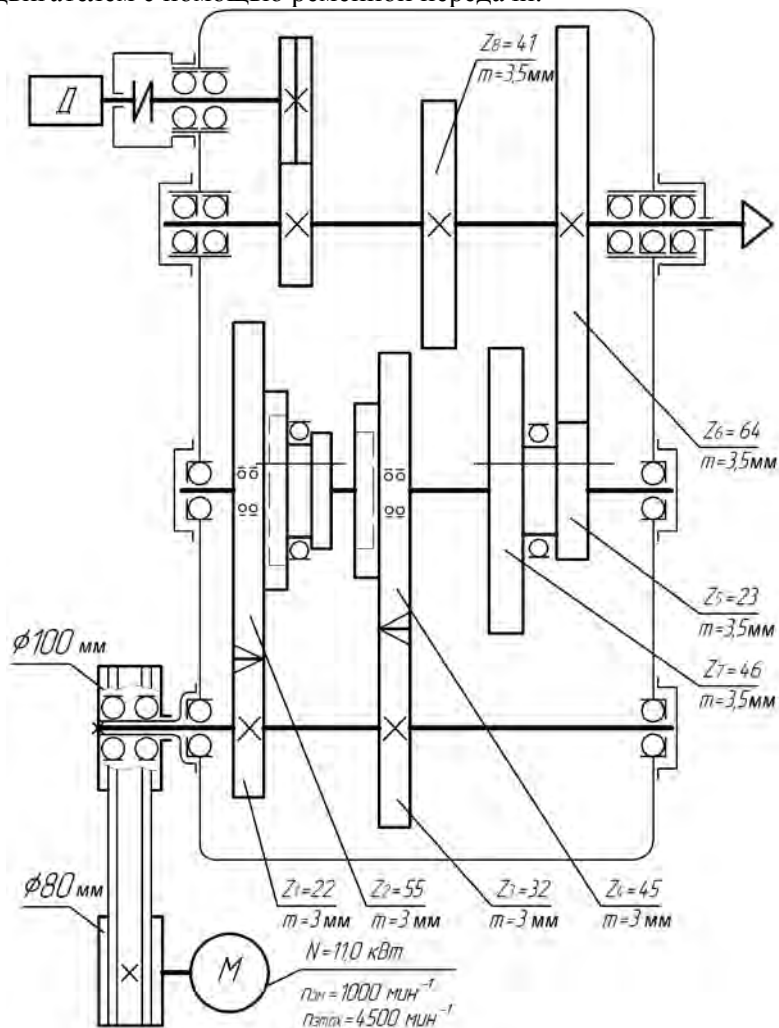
Кинематическая схема привода главного движения токарного станка с ЧПУ со встроенными в корпус шпиндельной бабки шпиндельным узлом и коробкой скоростей
